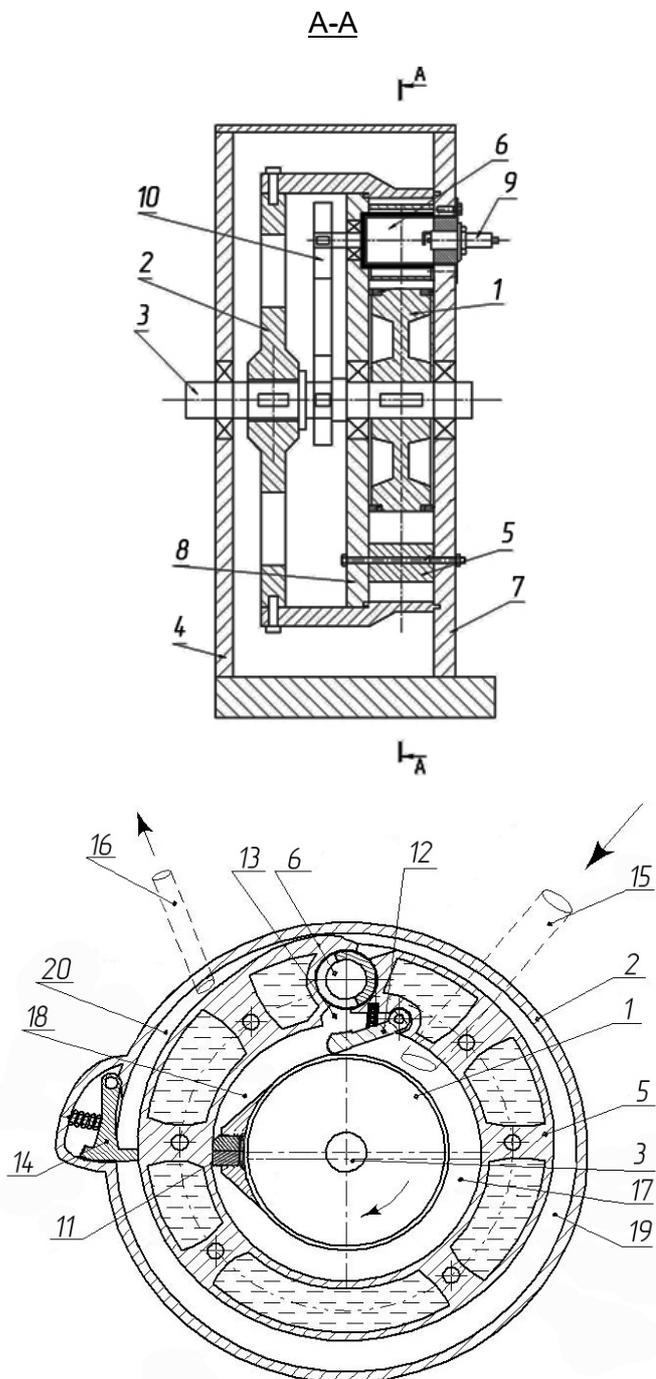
Схематичный разрез двигателя РДТ-3:
